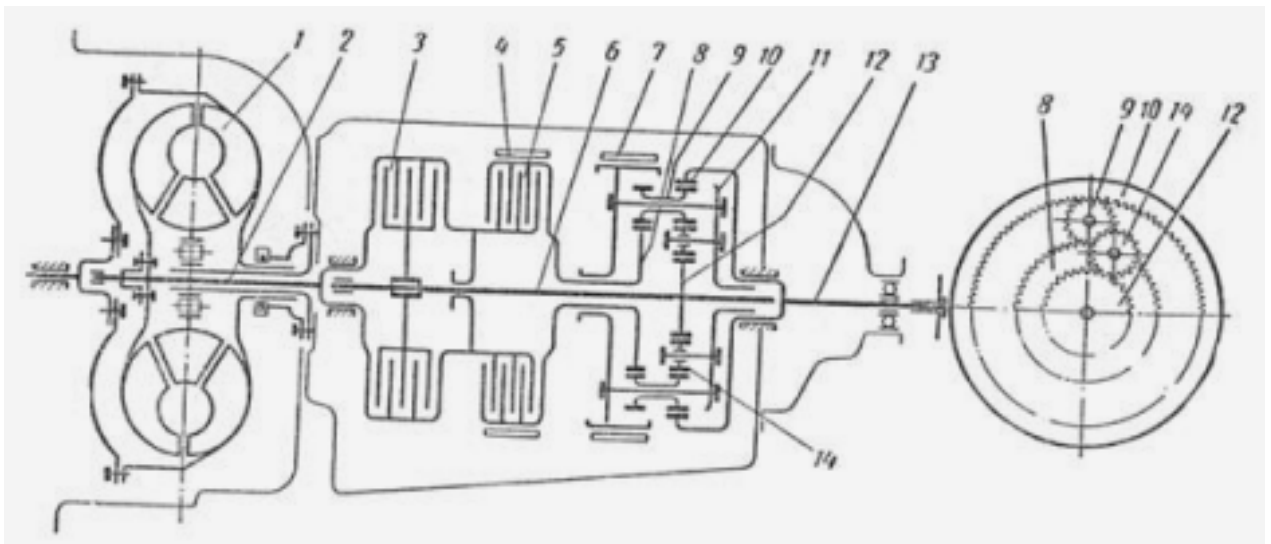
Схема работы автоматической передачи автомобиля: 1 - гидротрансформатор; 2 - ведущий вал; 3, 5 - переднее и заднее сцепление; 4, 7 - передний и задний тормоза; 6 - центральный вал; 8 - передняя солнечная шестерня; 9 - длинные сателлиты; 10 - коронная шестерня; 11 - каретка; 12 - задняя солнечная шестерня; 13 - ведомый вал; 14 - короткие сателлиты
